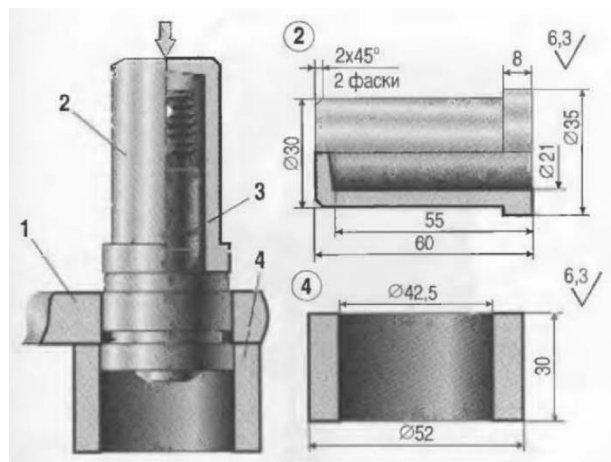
Випресовка шарнірів рульової тяги:
